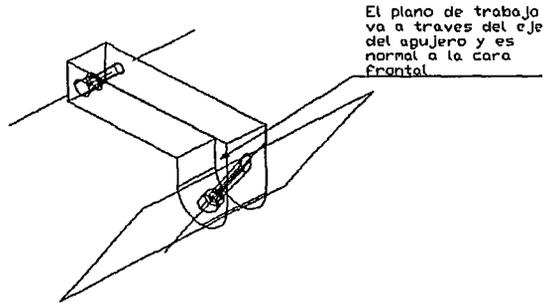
Plano restringido a un eje y normal a un plano (On Edge/Axis & Planar Normal).
